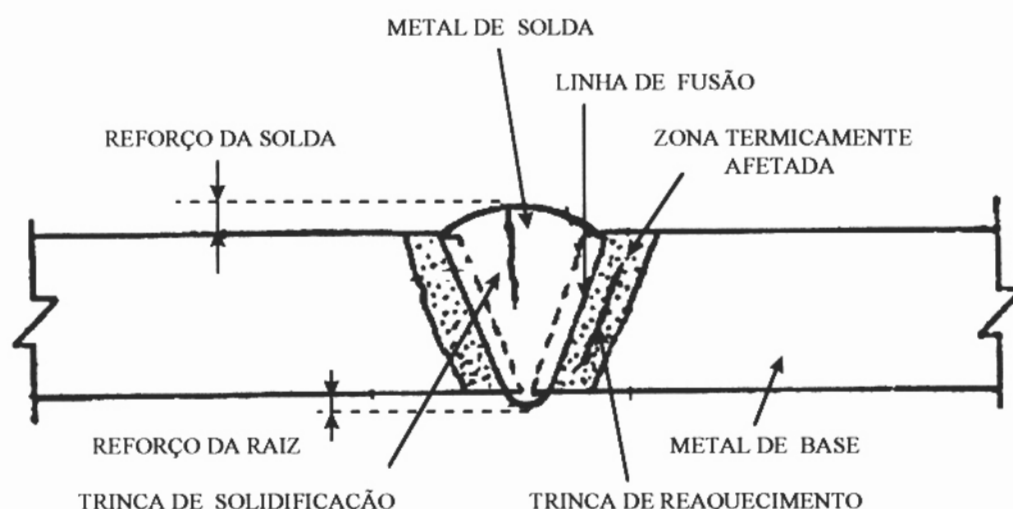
Zonas de uma junta soldada com as discontinuidades: trinca de solidificação e trinca de reaquecimento.
